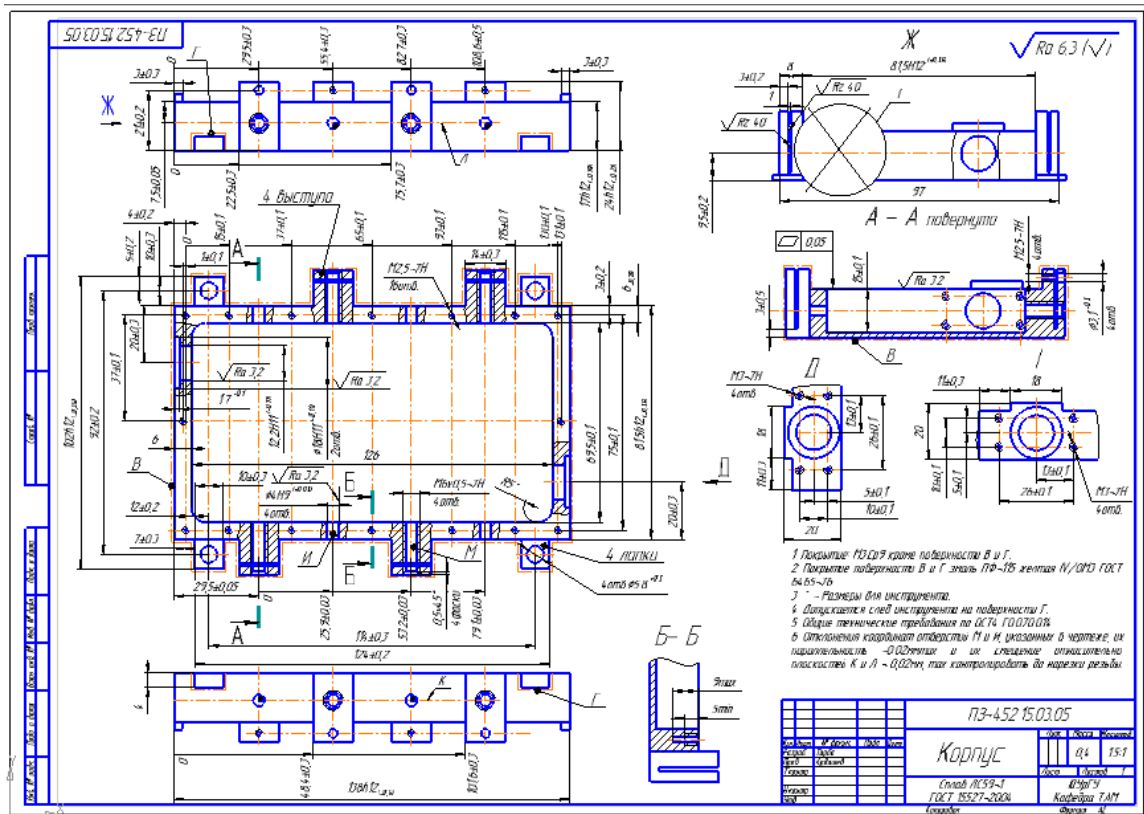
Чертеж детали «Корпус платы»
